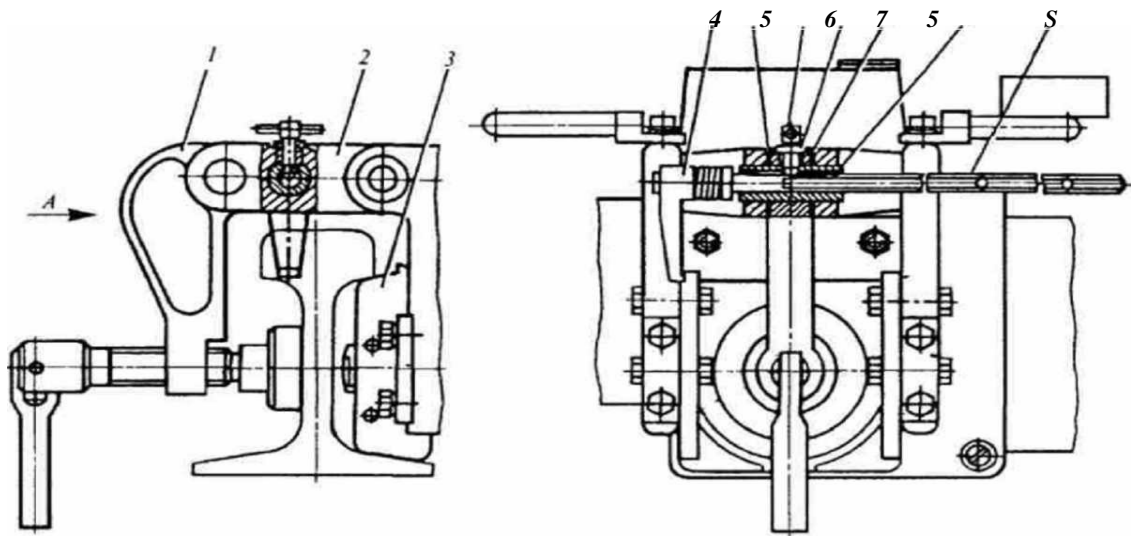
Приспособление для установки станка на рельс без предварительной разметки
